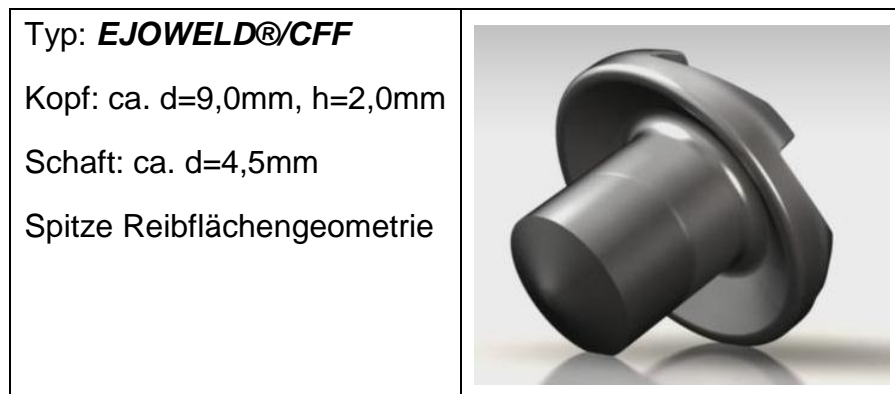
Hilfsfügeteil zum Reibelementschweißen EJOWELD®/CFF (Quelle: EJOT)
